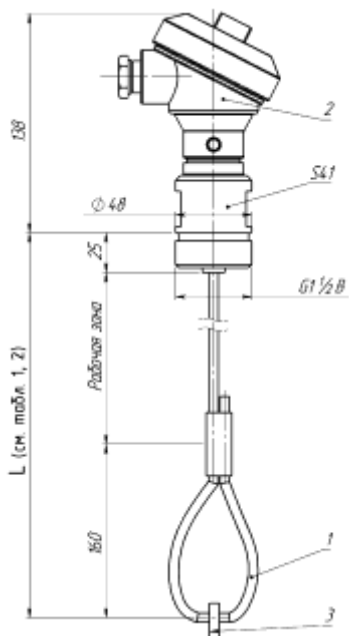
Габаритные и установочные размеры преобразователя передающего
